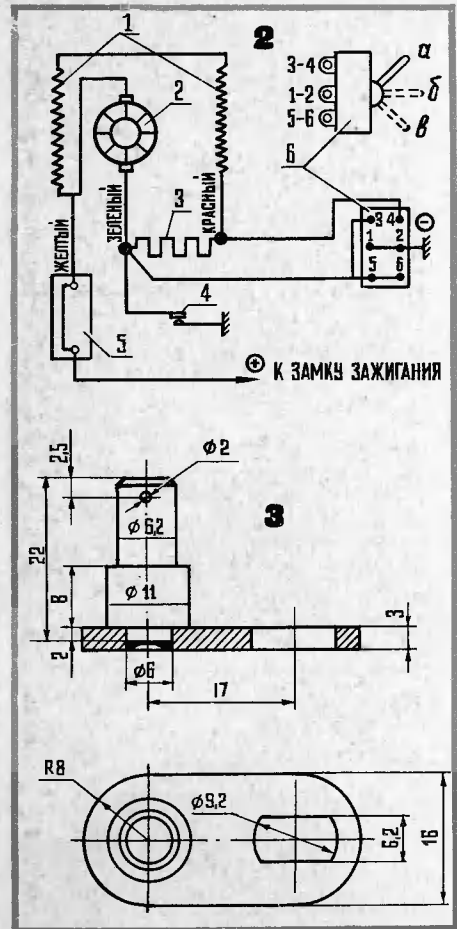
Электросхема стеклоочистителя: 1 — обмотка возбуждения двигателя; 2 — якорь; 3 — сопротивление; 4 — концевой выключатель; 5 — биметаллический предохранитель; 6 — выключатель.
